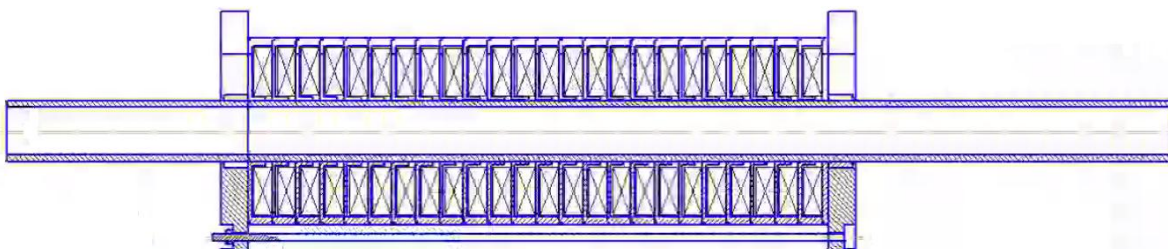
Цилиндрический линейный асинхронный двигатель.
